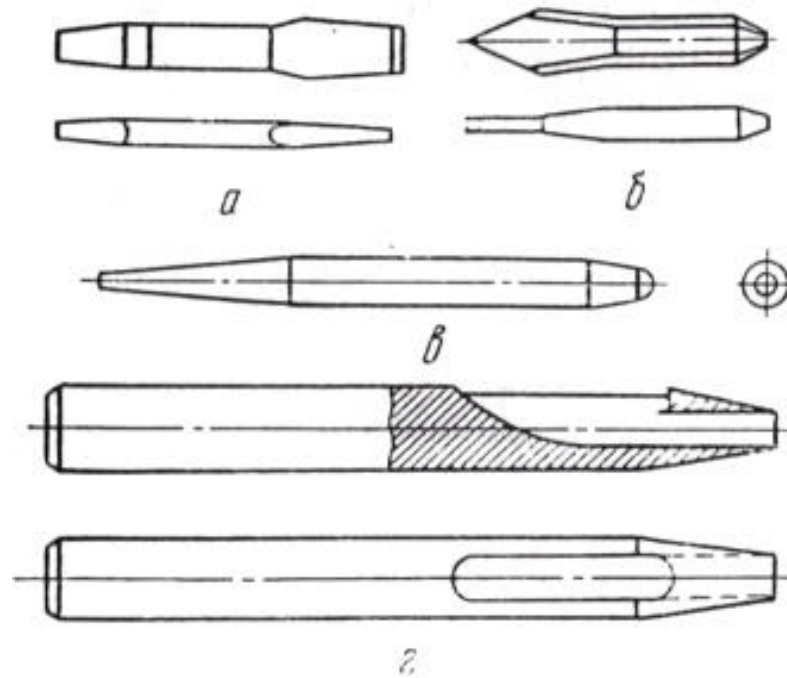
Інструменти для ручного вирубвання металу і пробивки отворів:
